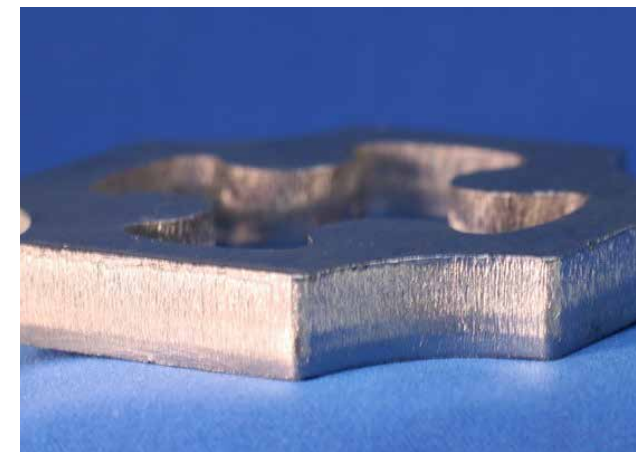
Пример детали, полученной с помощью лазерной резки из толстолистовой заготовки
